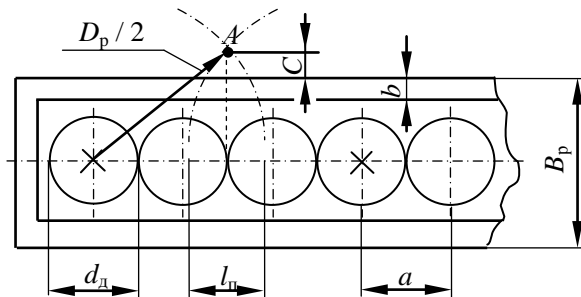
Схема к расчету необходимой величины перекрытия
